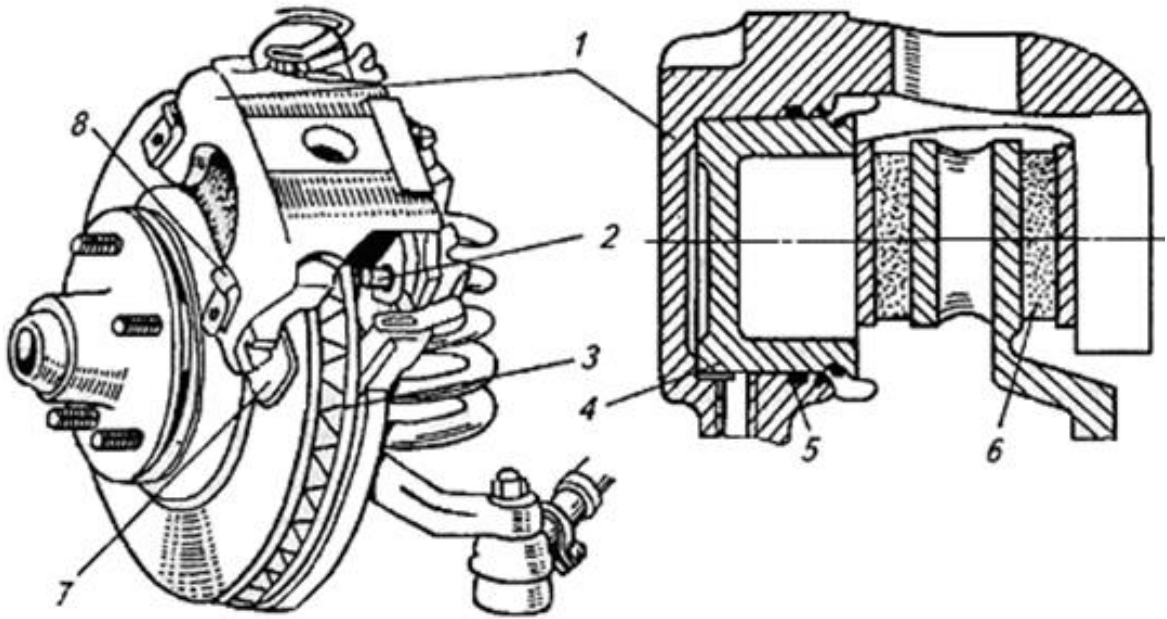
Дисковый тормозной механизм с плавающей скобой: 1 - скоба; 2 - направляющие штифты; 3 - суппорт; 4 - поршень; 5 - уплотнительное кольцо; 6 и 7 - колодки; 8 - пластинчатая пружина
